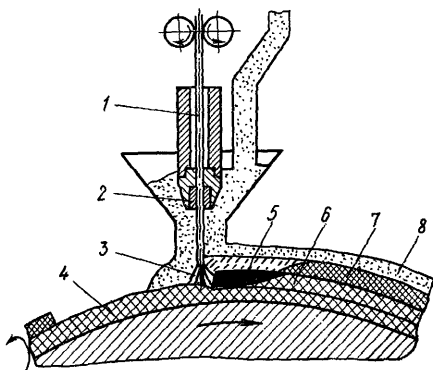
Схема процесса автоматической электродуговой наплавки вала под слоем флюса:
